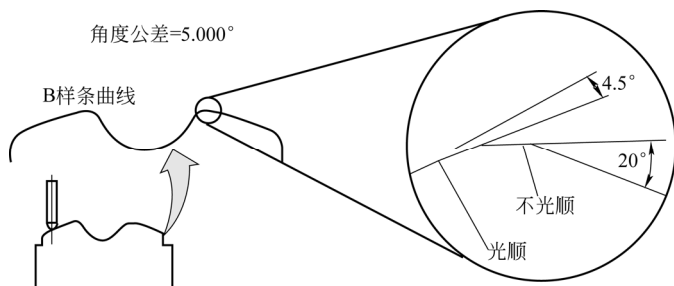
小于指定角度公差的角度将被光顺处理
